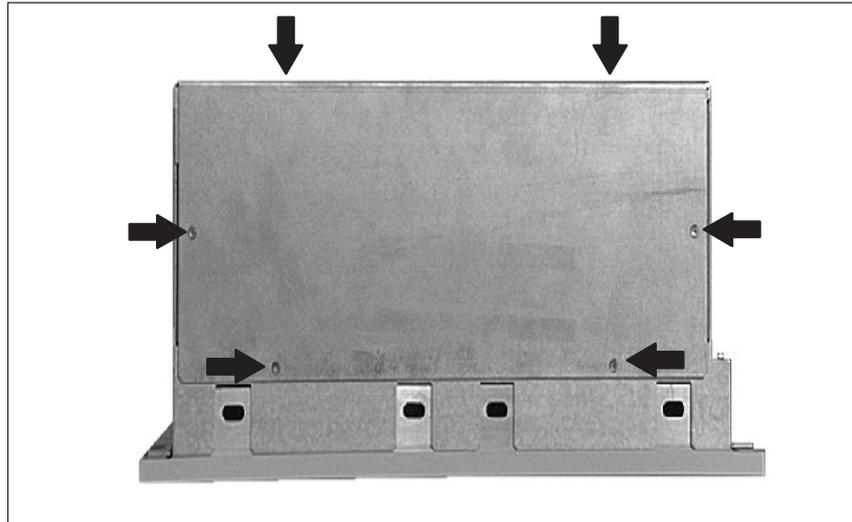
Entfernen des Deckels am Rechnergehäuse
